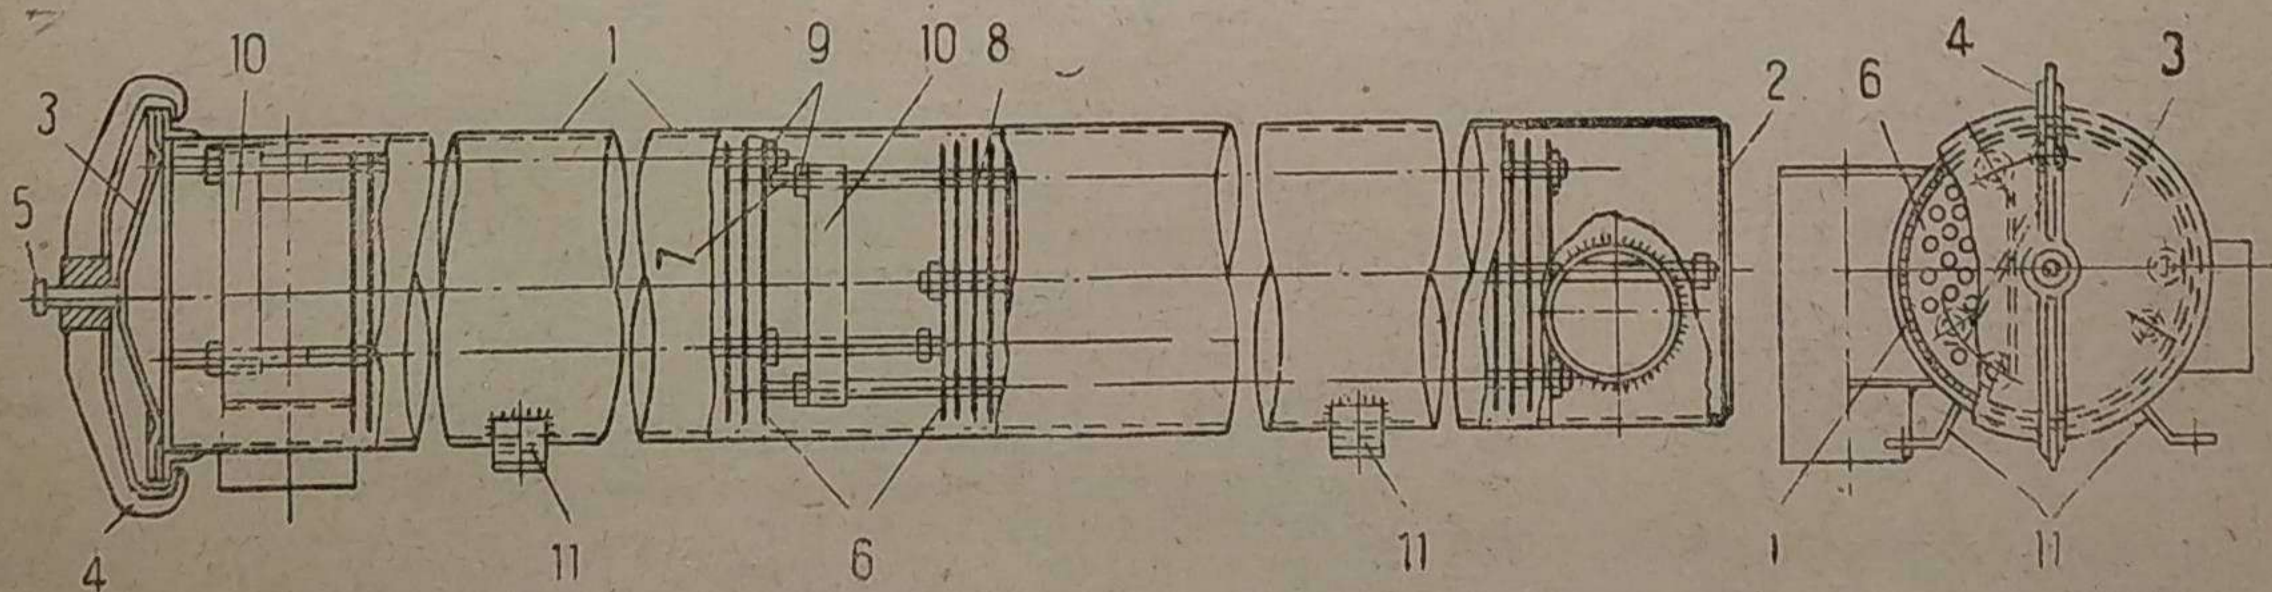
Горизонтальный очиститель грубой очистки газа установки ЗИС-21
